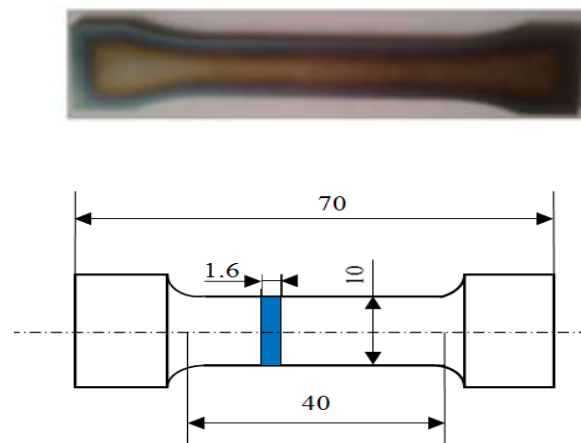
Forme et dimensions de l'éprouvette de traction.
